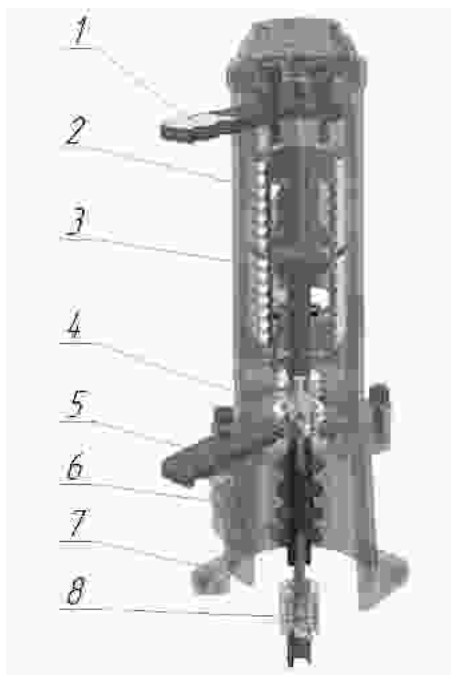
Вакуумный выключатель типа ВВУ-СЭЩ-ЭЗ-10-20/1600
